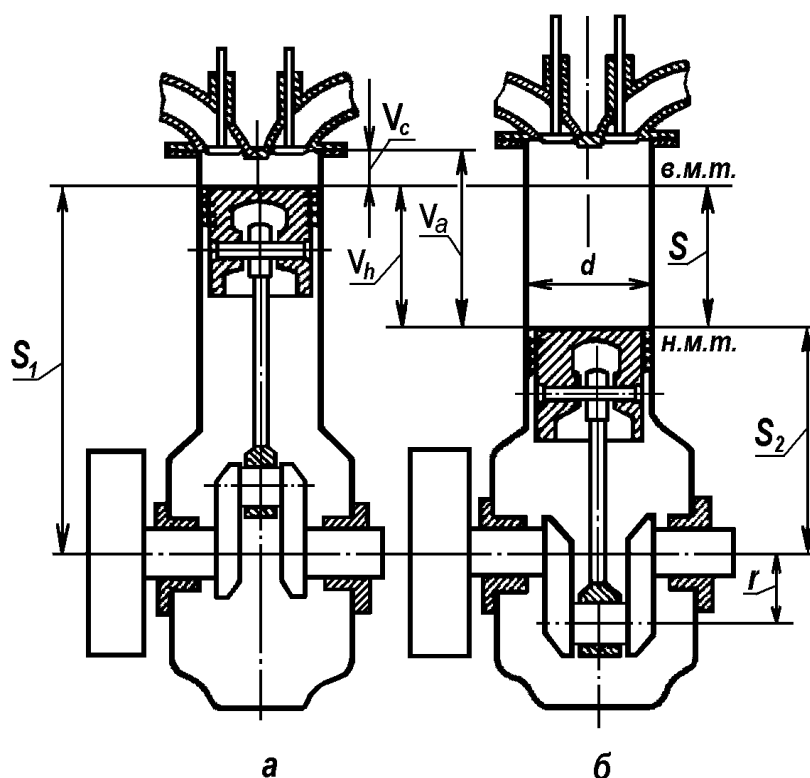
Схема и основные размеры поршневого двигателя внутреннего сгорания: а- поршень в в.м.т.; б- поршень в н.м.т.
